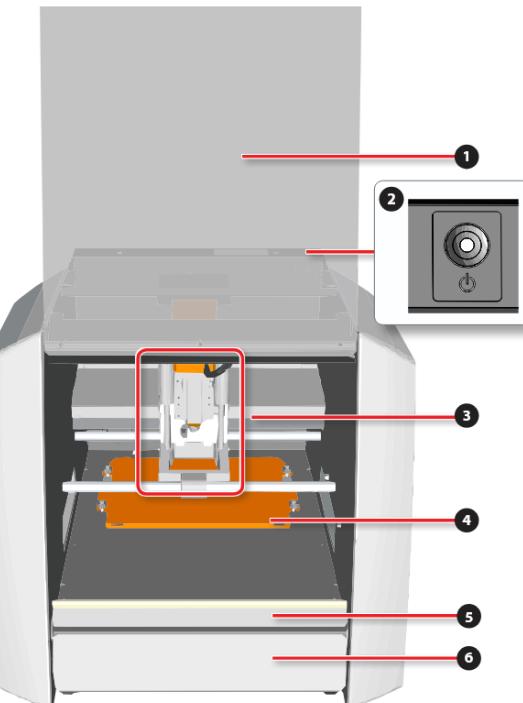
Máquina CNC SRM-20. Fuente: Roland DG Corporation
